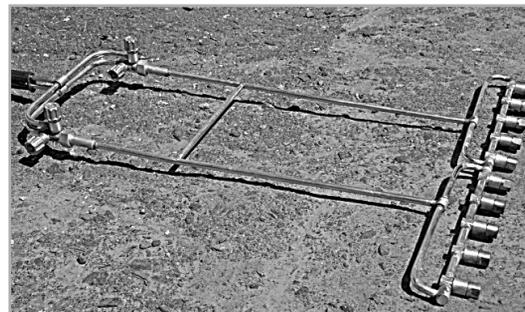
Горелка для нагрева рельсов ГЗУ6-ЖД
